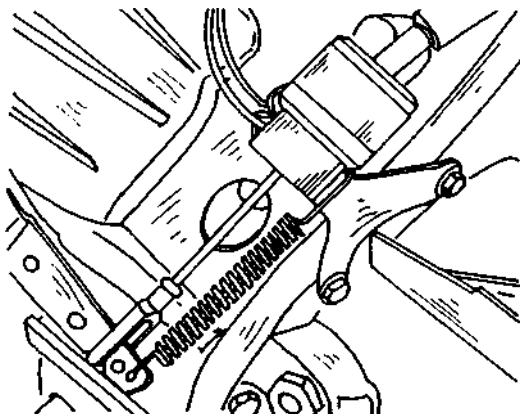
Uspořádání vysouvacího mechanismu spojky;
